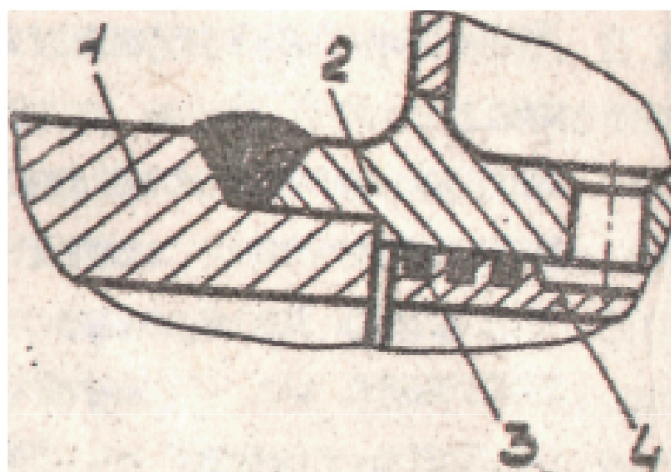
Соединение головки с корпусом камеры при установке коллектора для вывода охладителя: 1 - корпус головки, 2 - корпус коллектора, 3 - припой, 4 – стенка корпуса.
